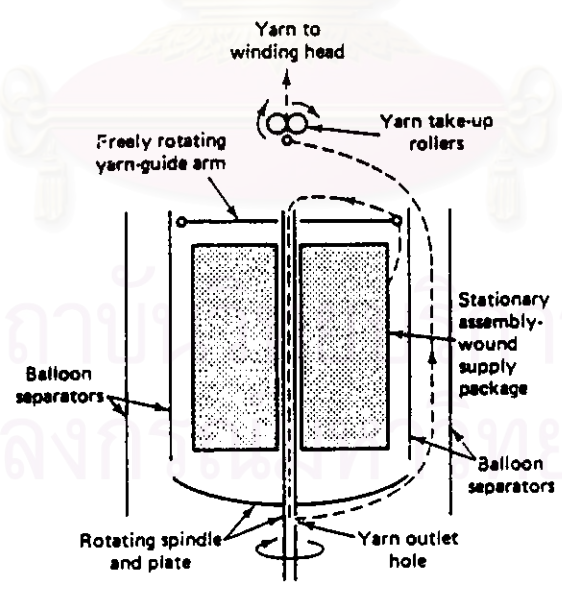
แสดงเครื่องกรอด้วย (Winding Machine)
